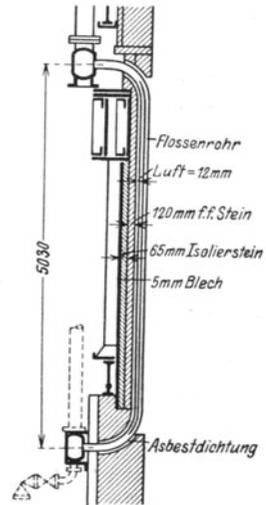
Schnitt durch eine wassergekühlte Wand für Dampfkessel nach Combustion Engineering Co. 1)
